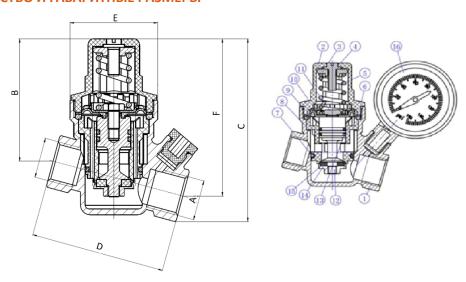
Устройство и габаритные размеры редукционного клапана ДУ 15 – 25
